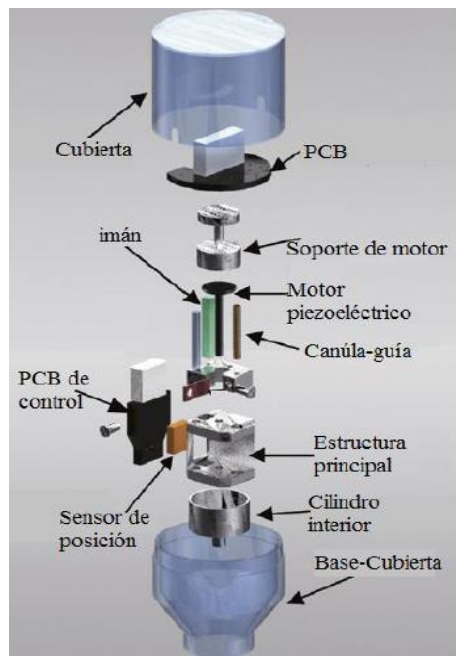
Vista explosiva del Microdrive con sus componentes principales [11].
